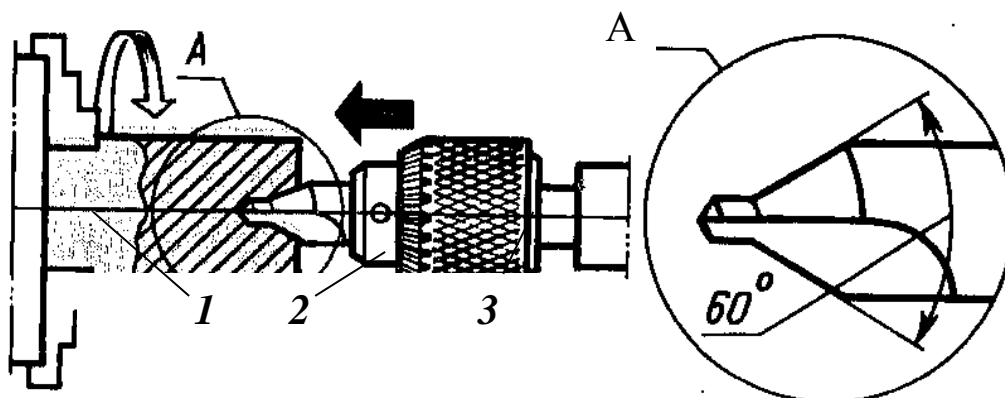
Обработка центровых отверстий: 1 – заготовка; 2 – патрон сверлильный и сверло; 3 – пиноль задней бабки
